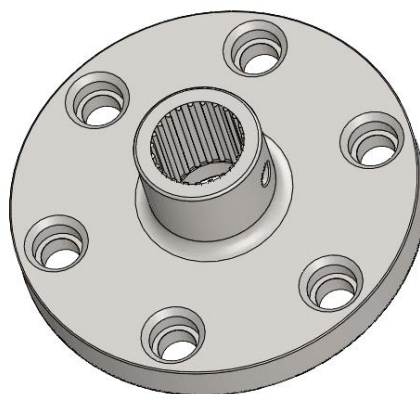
Útil de fixació tornejat per transmetre el moviment a partir de l'eix del motor elèctric i unir el conjunt motor i placa adaptador amb el volant d'inèrcia i la transmissió.
